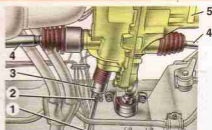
Вид снизу на коробку передач: 1 – трос привода рычага переключения передач; 2 – хомут; 3 – шарнир штока выбора передач; 4 – валы привода передних колес; 5 – коробка передач
